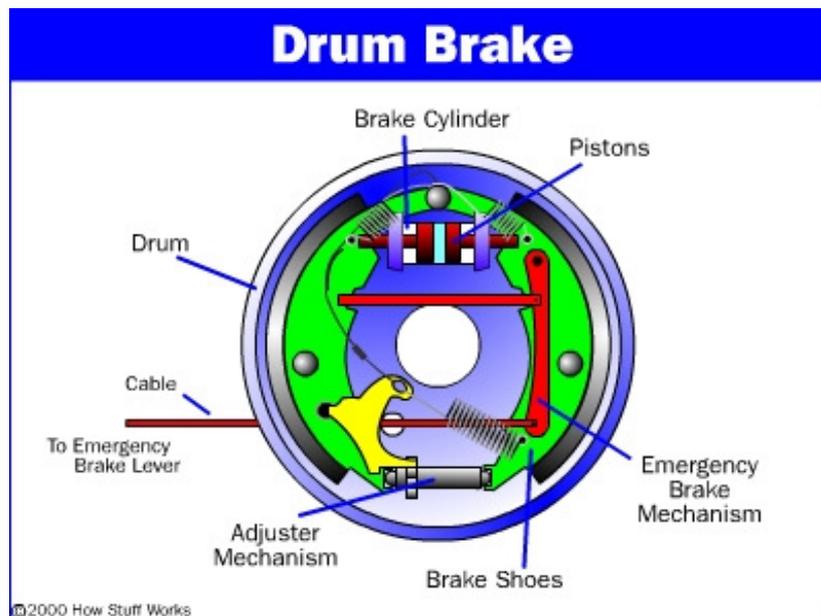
Imagen Frenos de Tambor⁶³.
